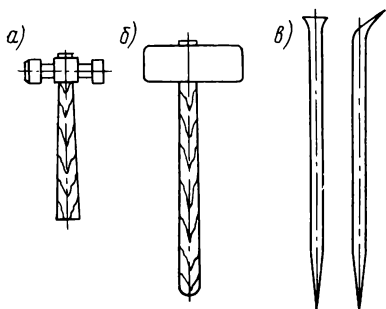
Ручной инструмент сборщика: а — молоток; б — киянка; в — сборочный ломик.
